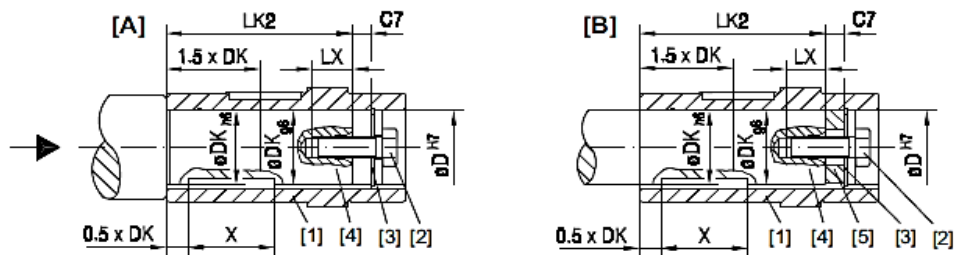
Eje de la máquina con tope (A) y sin tope (B)
